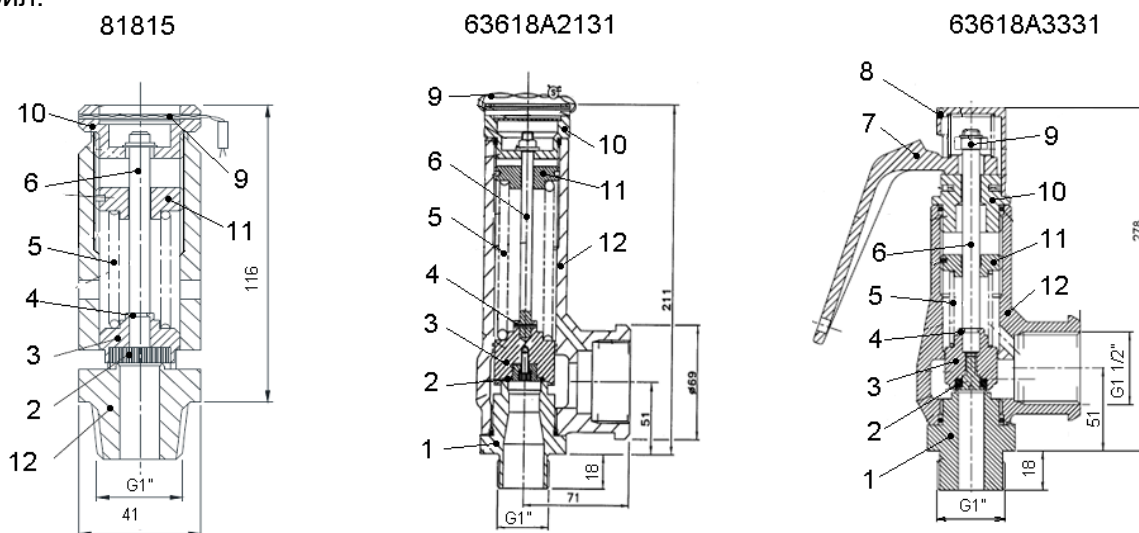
Клапан предохранительные типа RA 81815 и 63618: 1 – впускное седло; 2 – уплотнение; 3 – внешний плунжер; 4 – штифт-фиксатор штока; 5 – пружина; 6 – шток; 7 – рычаг; 8 – колпачок защитный; 9 – проволока и пломба; 10 – крышка подъемного устройства; 11 – регулятор; 12 – корпус.
